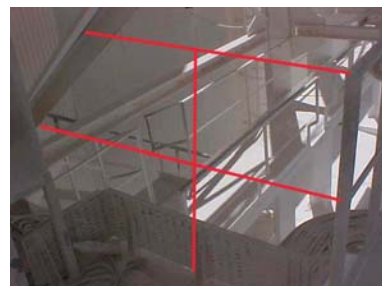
ELEVADOR/EC-2201. Falta sistema de enclavamiento en el resguardo.
